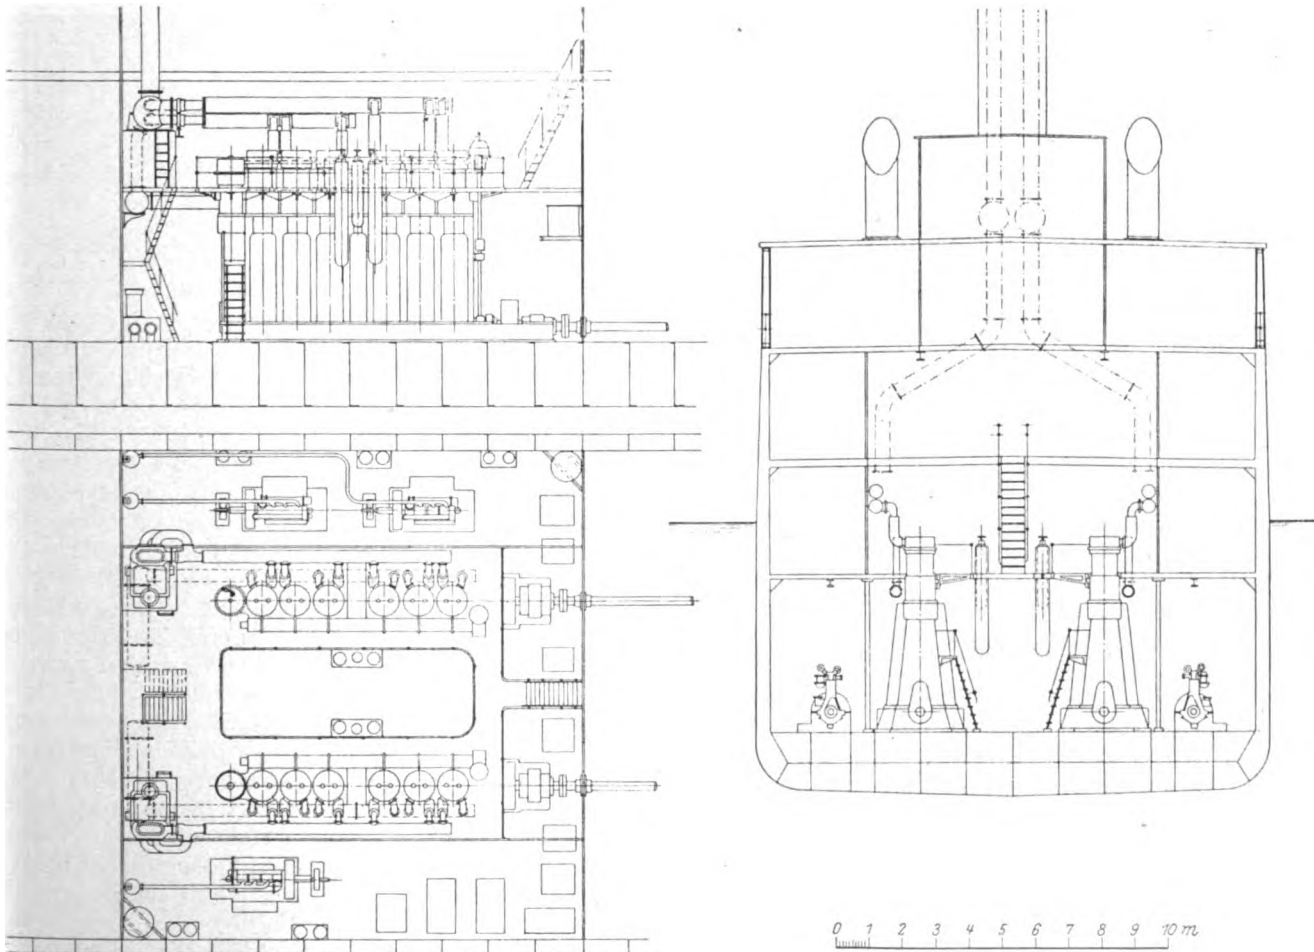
Dieselmotorenanlage mit Auspuff-Gasturbinen-Aufladung für ein Zweischaubenschiff
